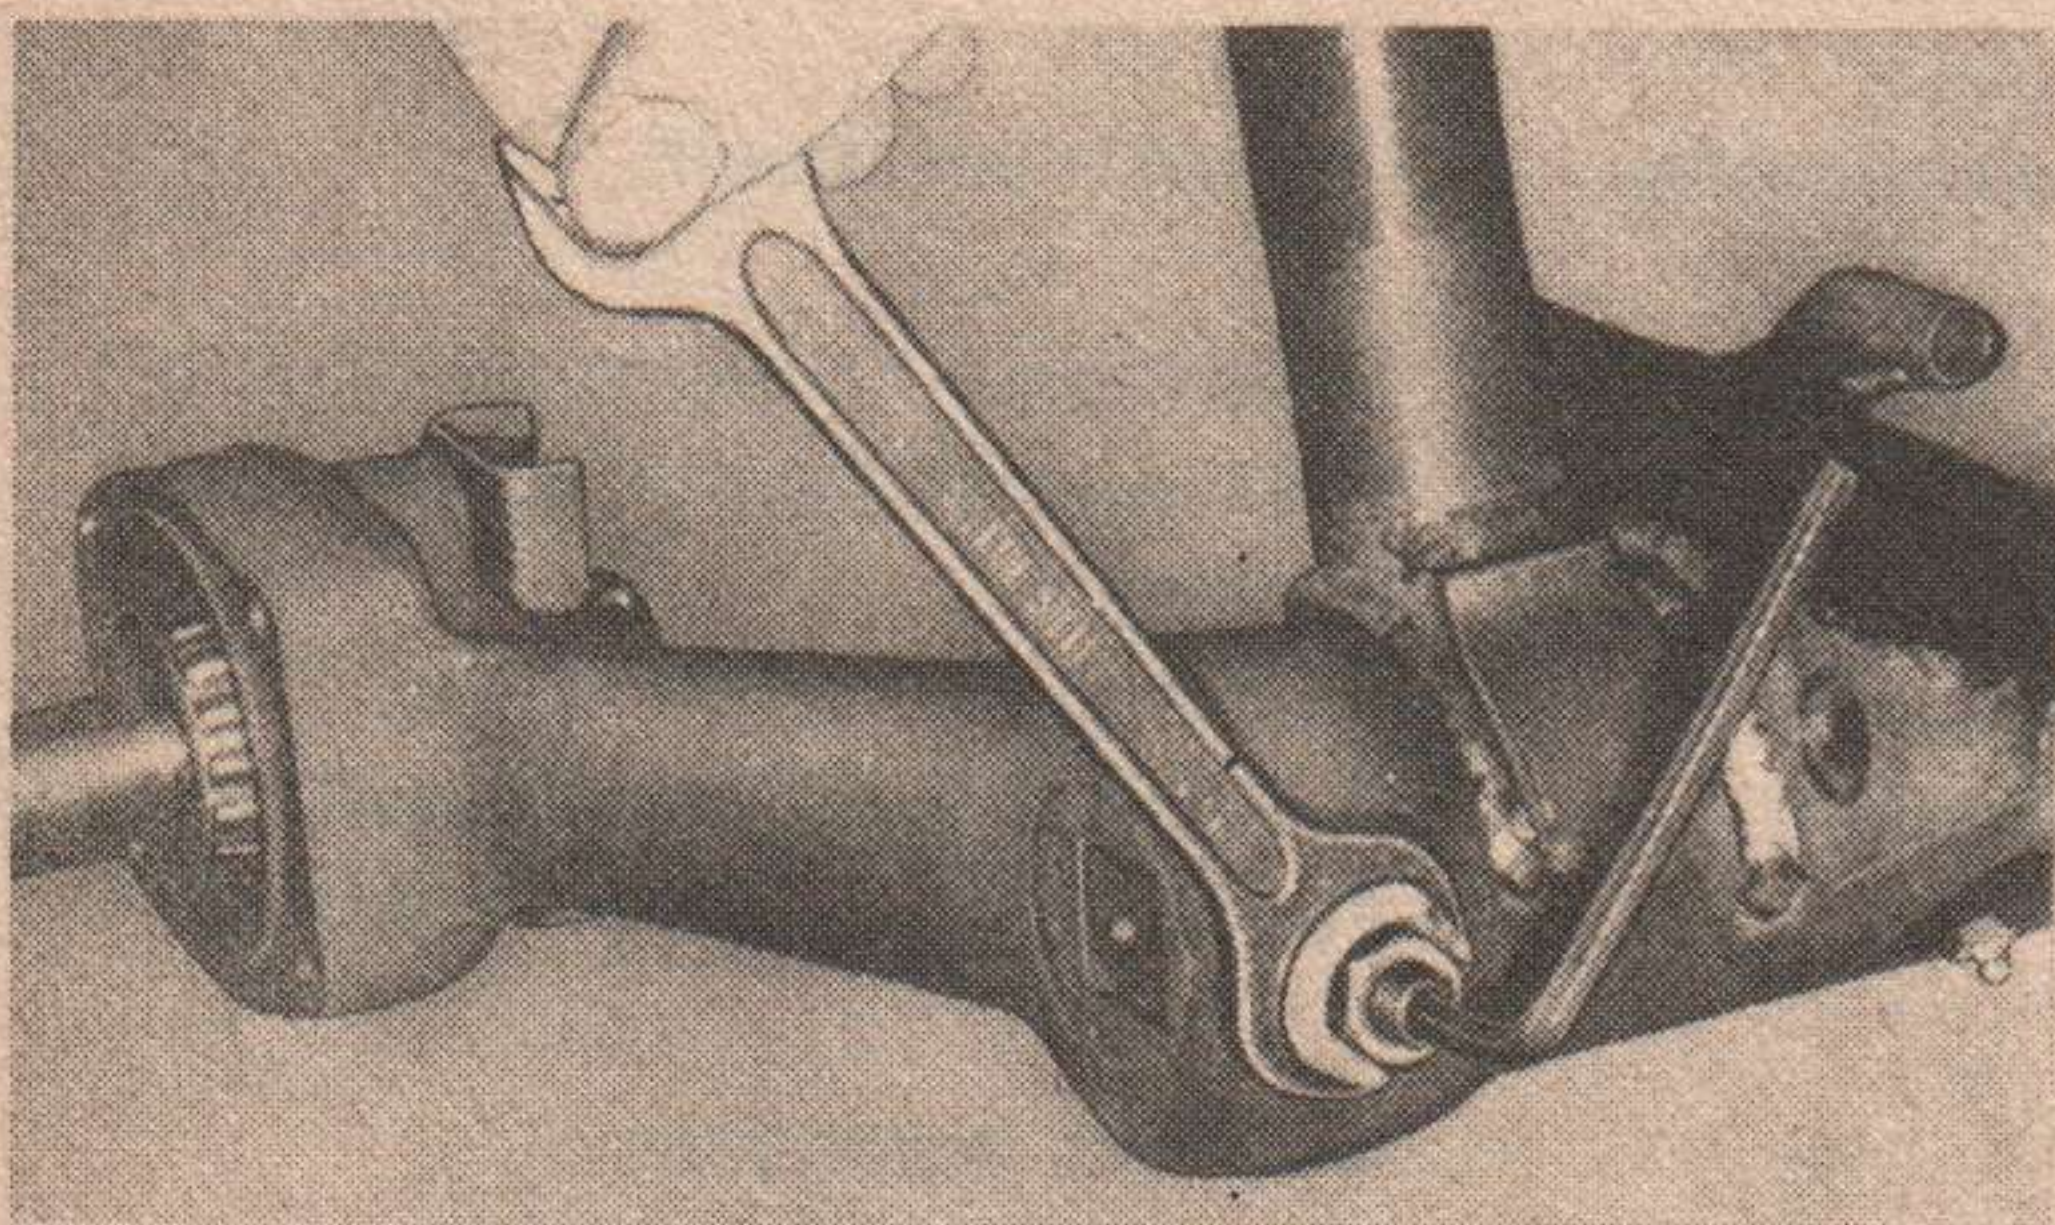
Lösen des M-12-Gewindestiftes durch Festhalten des Stiftes mit einem Innensechskantschlüssel und Aufdrehen der M-12-Mutter mit einem Gabelschlüssel SW 19
